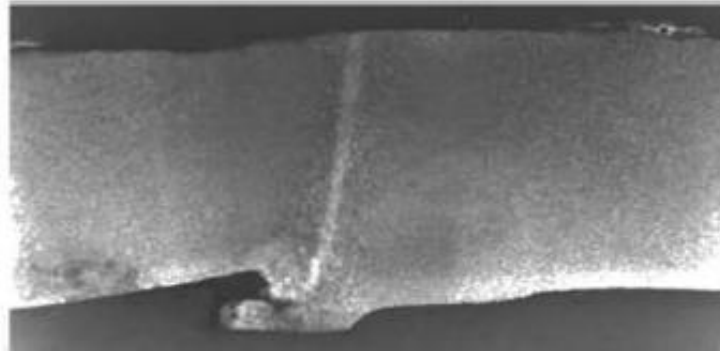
Foto de sección de soldadura de un caño [3]
